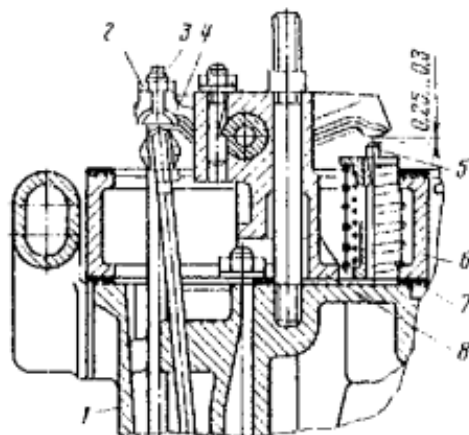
Схема регулювання зазорів у клапанному механізмі:
